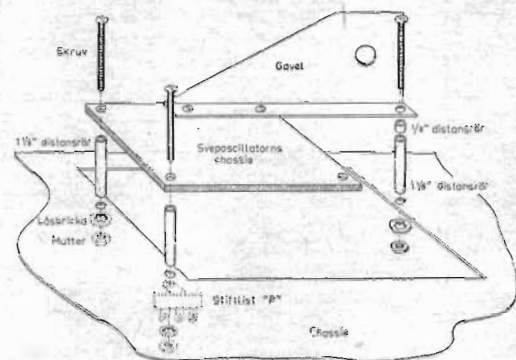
Sveposcillatorn monteras på huvudchassiet på detta sätt.
